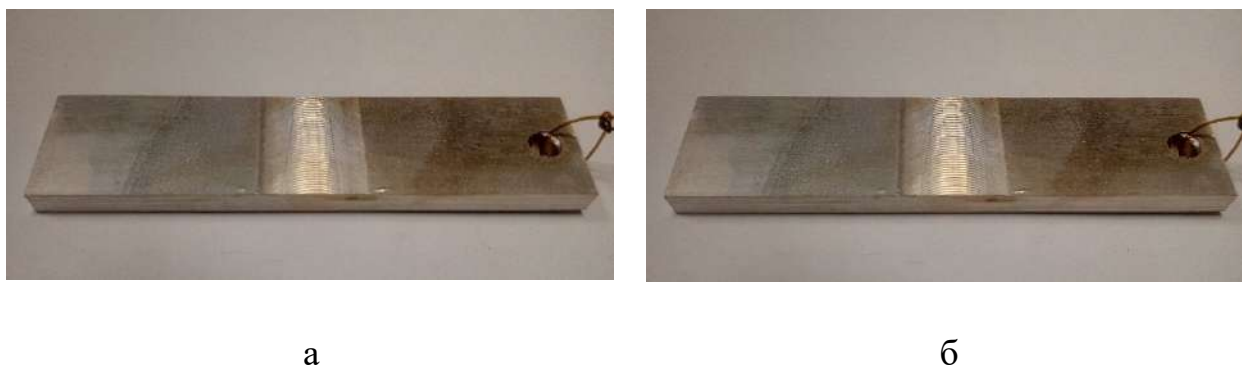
Внешний вид образцов сварных соединений, выполненных
